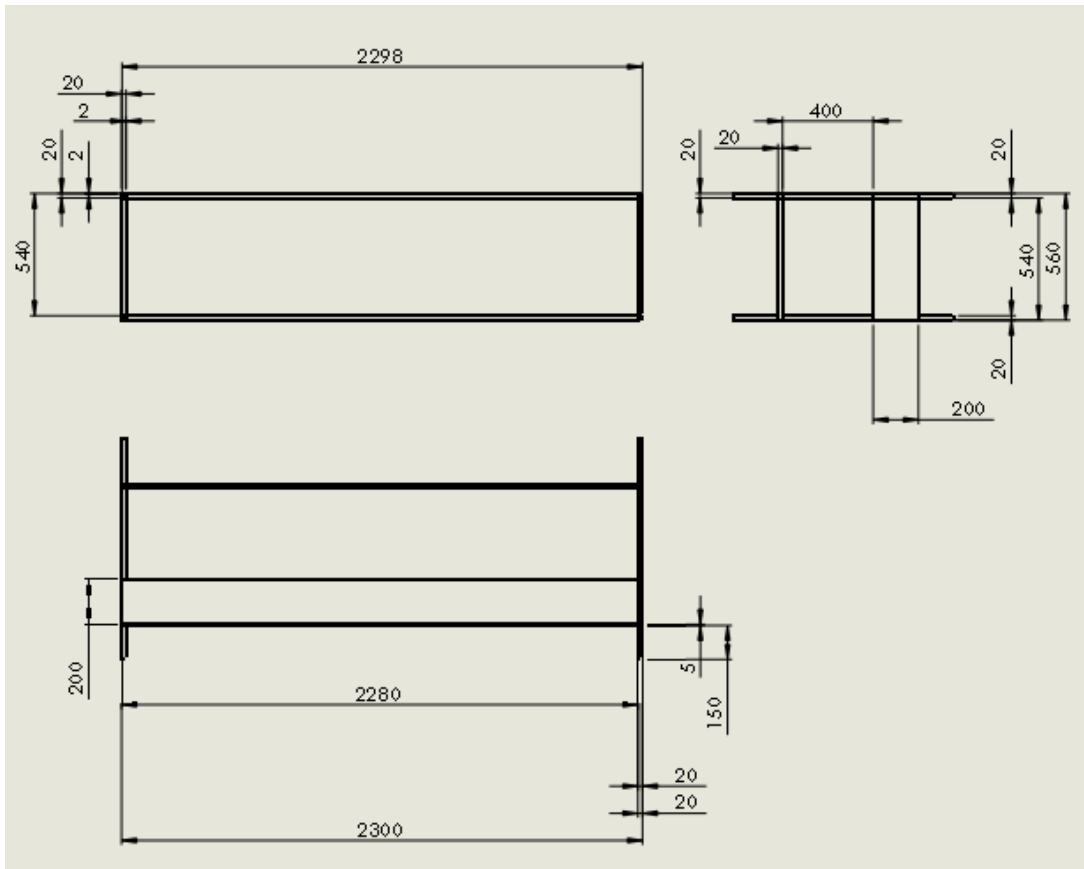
Plano de Construcción Estructuras Metálicas (mm).
